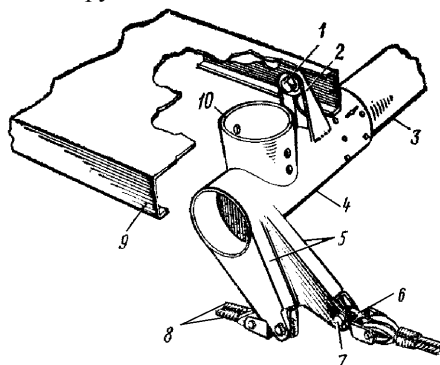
Поперечная труба с узлами и ее подвеска к силовой балке:
